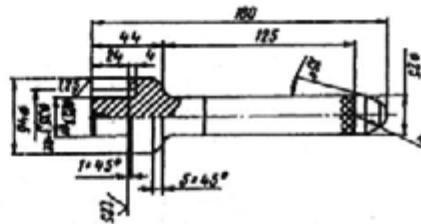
Оправка для запрессовки подшипников дифференциала:
